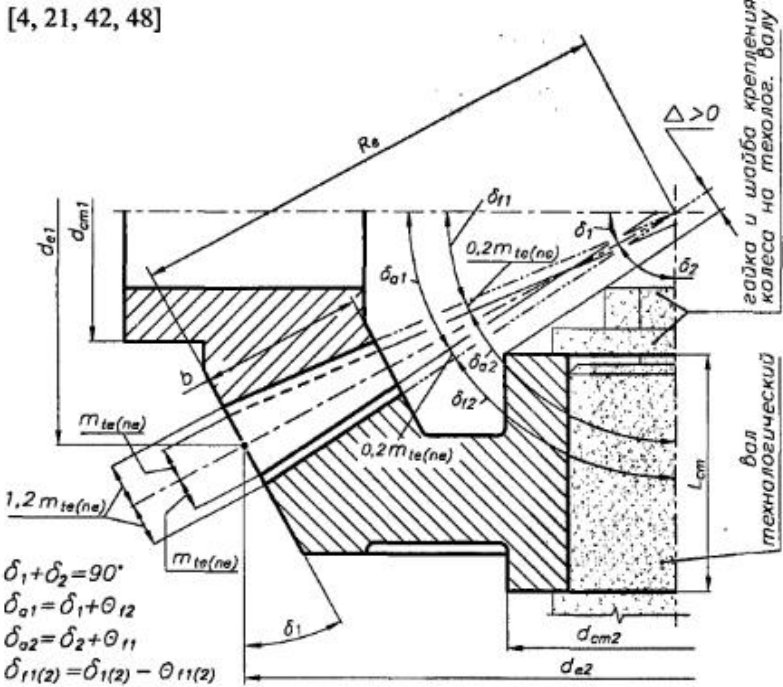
Зубчатые колеса с осевой формой зуба I и постоянным радиальным зазором по ширине зубчатого колеса
